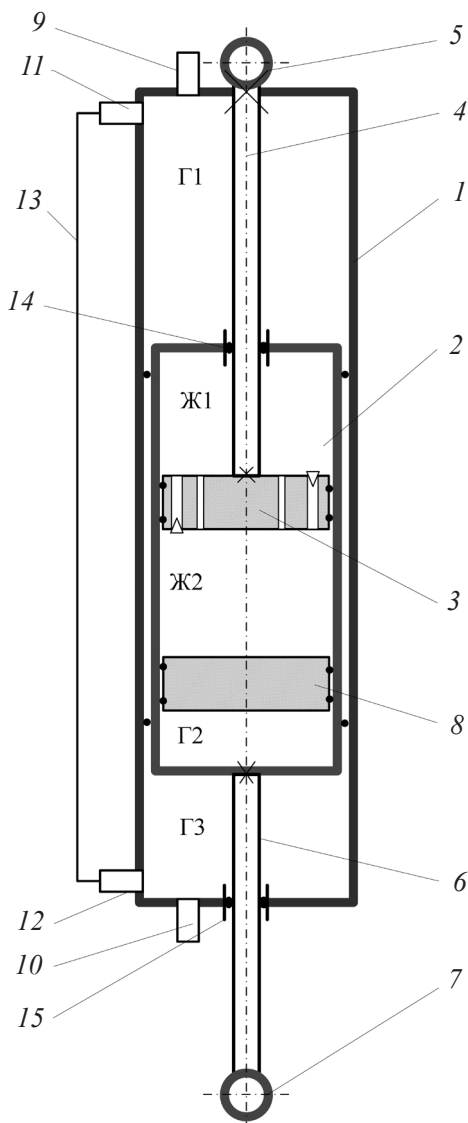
Конструкция амортизатора: Ж1, Ж2 – гидравлические полости; Г1–Г3 – газовые полости; 1 – внешний цилиндрический резервуар (цилиндр); 2 – рабочий цилиндр; 3 – гидравлический поршень; 4, 6 – шток; 5, 7 – проушины крепления; 8 – компенсационный поршень; 9, 10 – ниппель; 11, 12 – предохранительные клапаны; 13 – соединительный трубопровод камер Г3 и Г1; 14, 15 – уплотнительно-направляющие втулки
